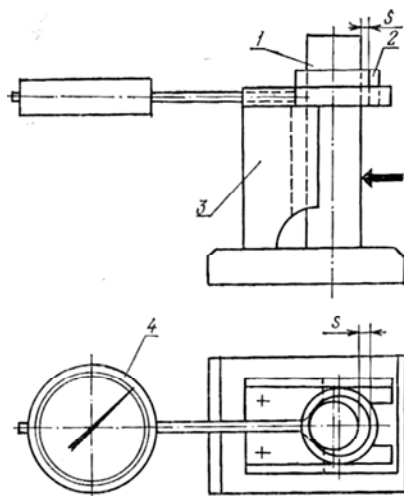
Схема приспособления для измерения зазора в сборочной единице:
